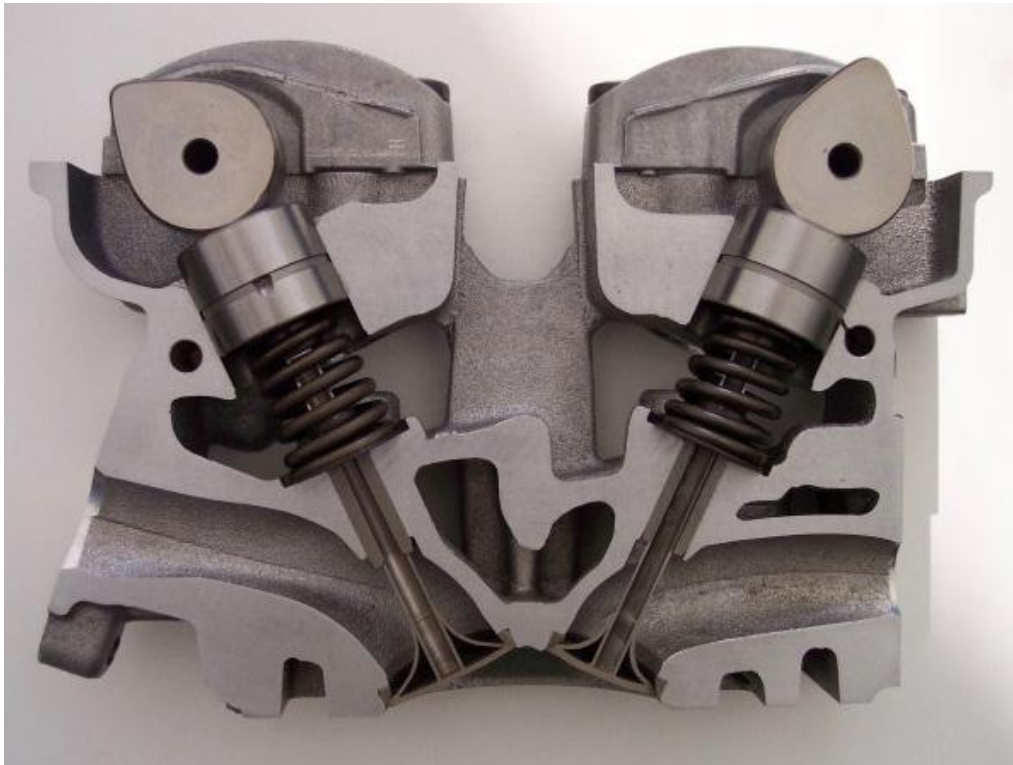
Газораспределительный механизм с подвесными клапанами, двумя распределительными валами, расположенными в головке блока цилиндров, и толкателями, расположенными над клапанами
